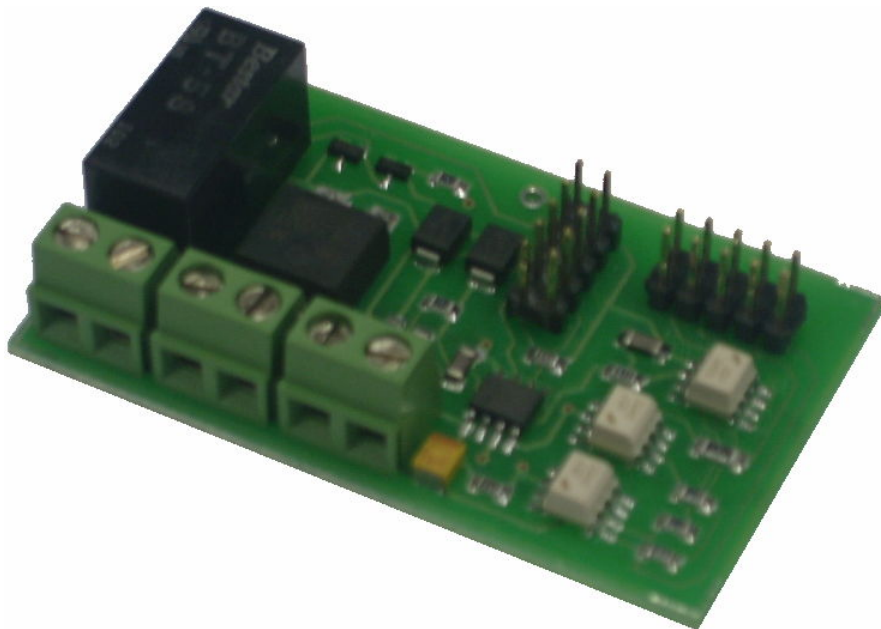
Внешний вид «Контроллера TOUCH-MEMORY для БДК-Л»
